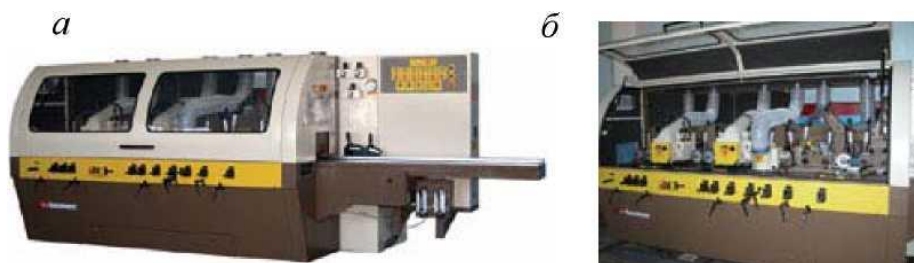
Чотирибічний поздовжньо-фрезерний верстат:
